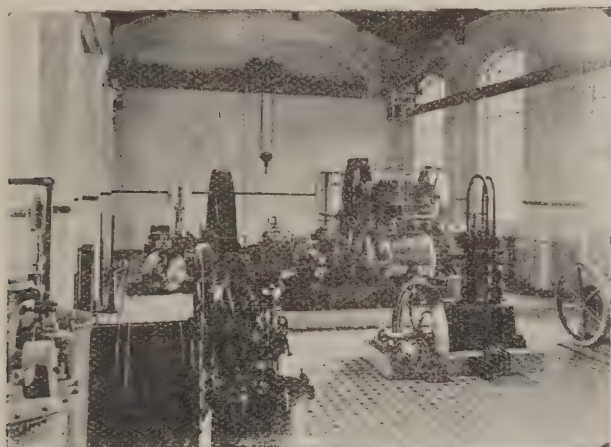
Institut de Mécanique. — Salle des Machines.
